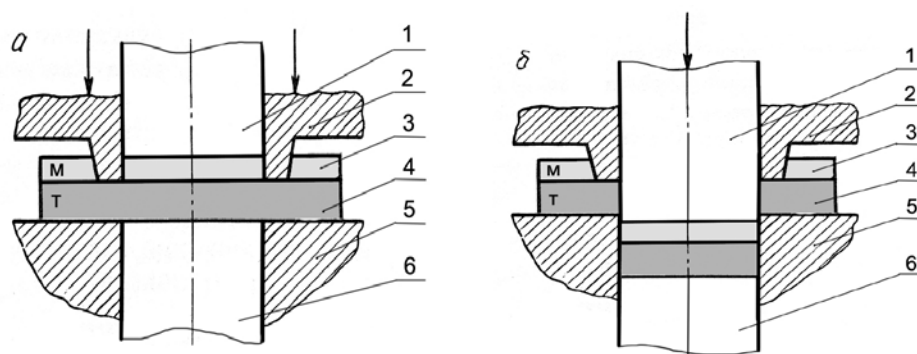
Схема чистовой вырубки листовых биметаллов встречными матрицами
